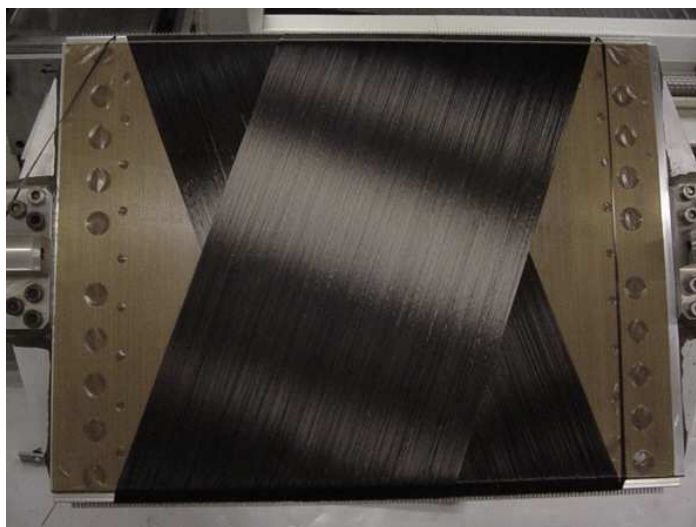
Etapa do processo de bobinagem a -20° da segunda camada de reforço de fibra de carbono para fabricação de placa a $\pm 20^{\circ}$ na direção do eixo transversal do mandril.
